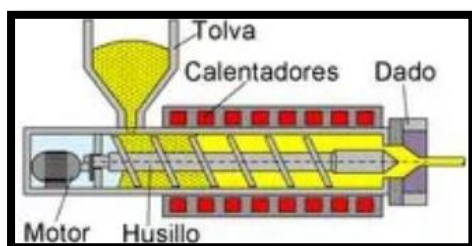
18. Composición de las partes internas en la máquina de extrusión.
